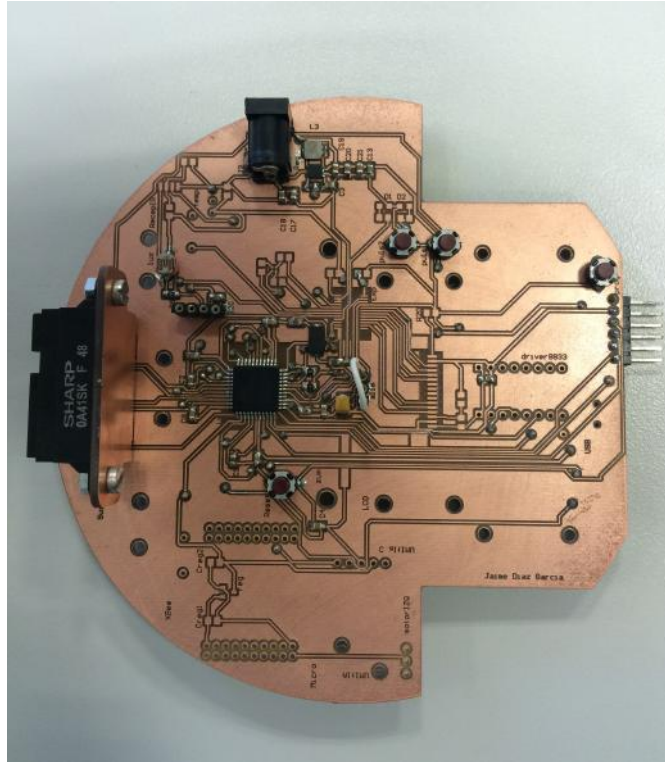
Plataforma robótica durante la fase de montaje de componentes
